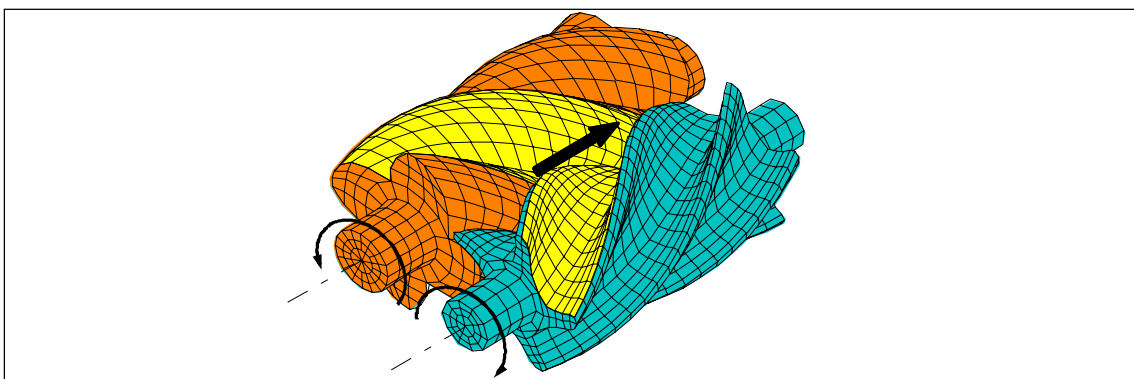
Arbeitsspiel des Schraubenmotors – Expansion
